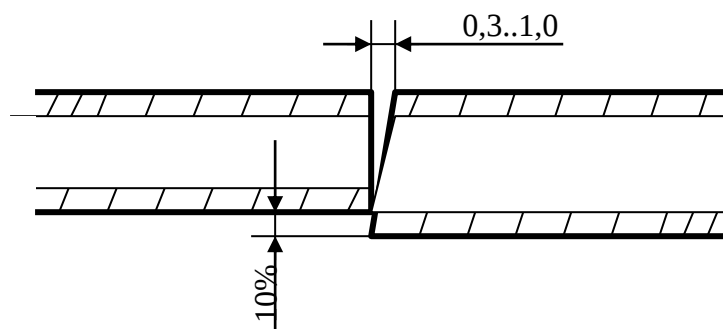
Допуски на смещение и зазор свариваемых поверхностей
